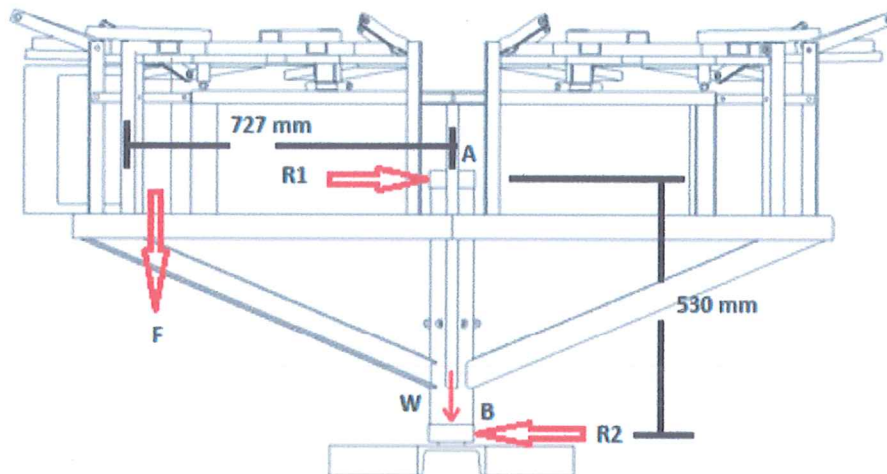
Cargas actuantes para la Selección de Rodamientos.
